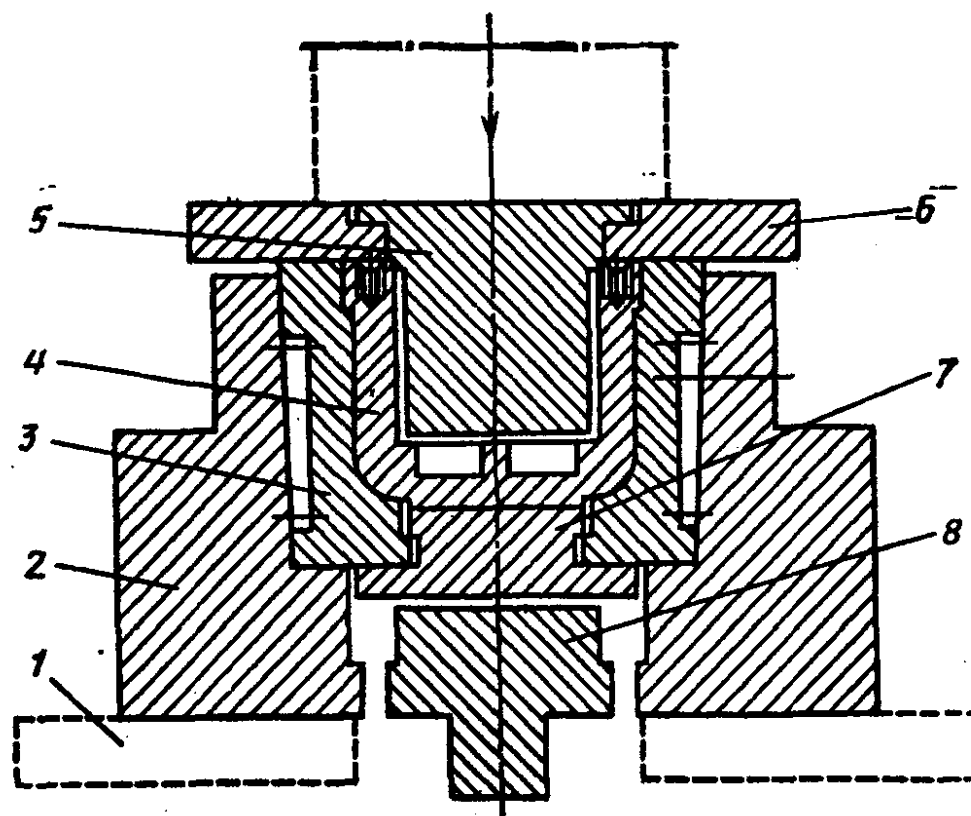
Схема гарячого пластичного деформування корпусу шестеренного насоса:
